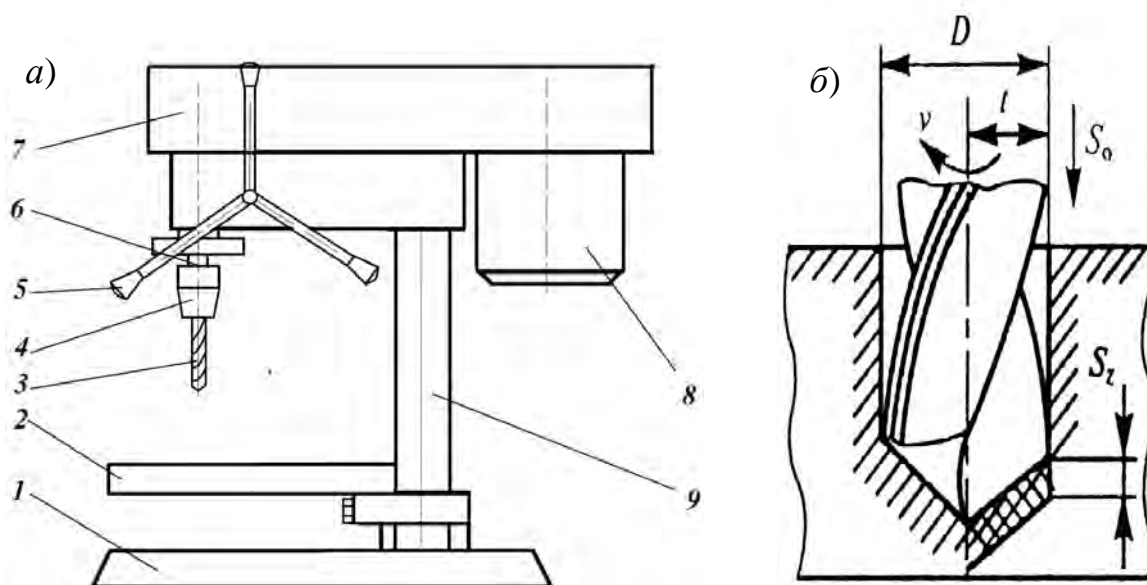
Схема настольного сверлильного станка (а) и элементов режима резания при сверлении (б)
